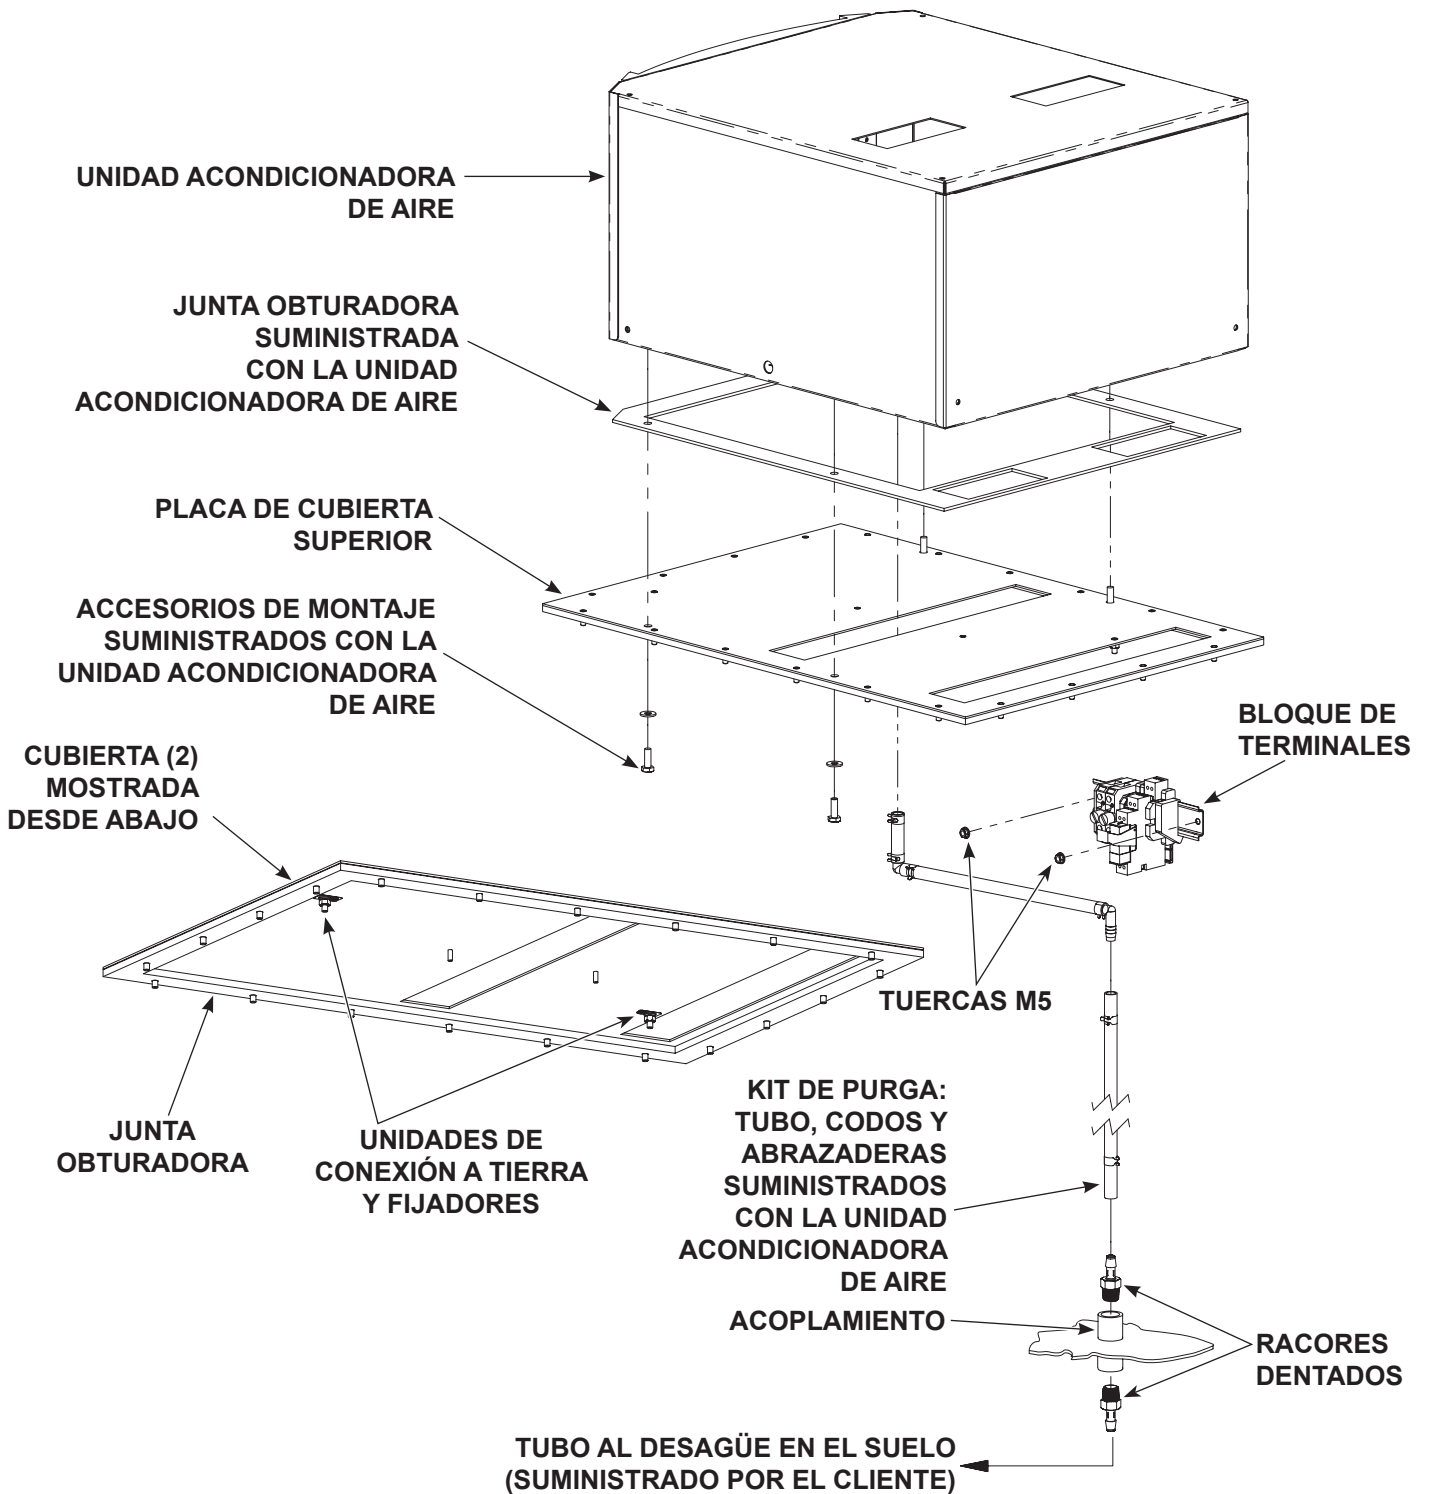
Instalación mecánica del acondicionador de aire opcional
